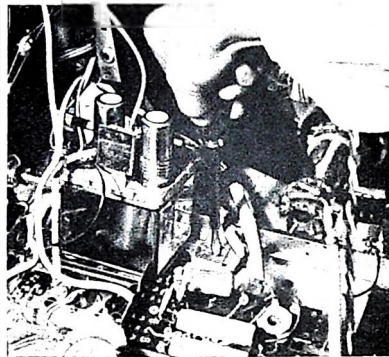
Der VHF-Kanalwähler des Chassis „FE 212“ ist mit nur einer Schraube am Chassis befestigt
